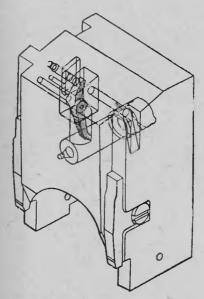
Положение деталей ударного и предохранительного механизмов при сборке
